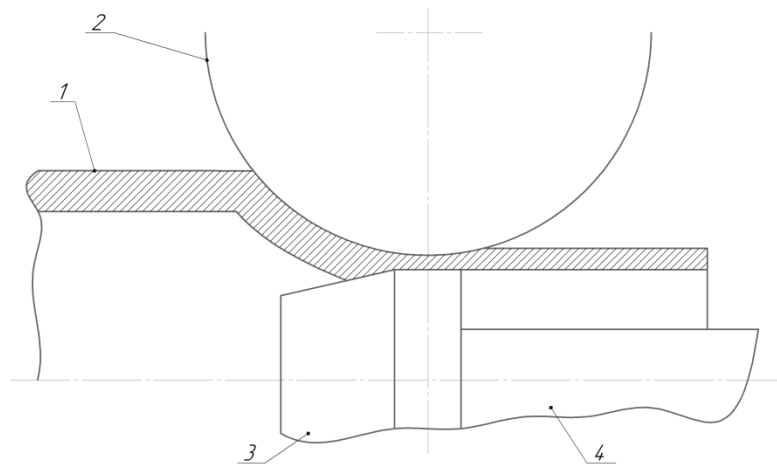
Прокатування заготовок на автоматичних станах:
